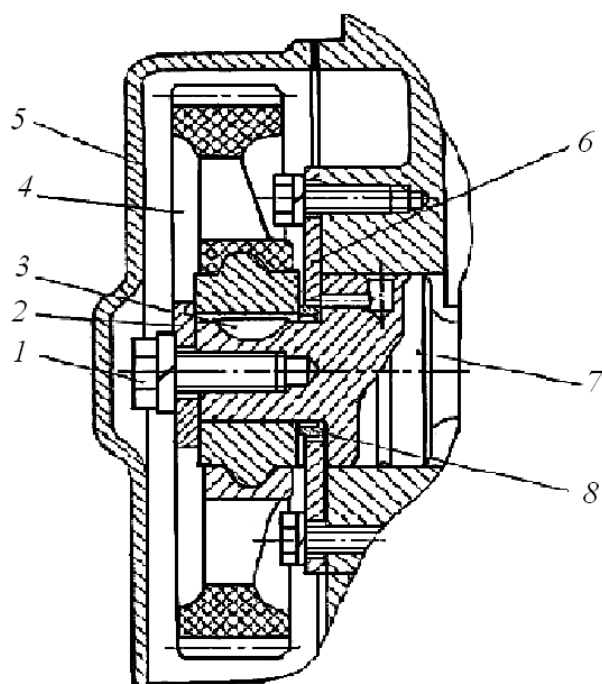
Привод распределительного вала: 1 – болт; 2 – шайба; 3 – шпонка; 4 – шестерня; 5 – крышка распределительных шестерен; 6 – упорный фланец; 7 – распределительный вал; 8 – распорная втулка
